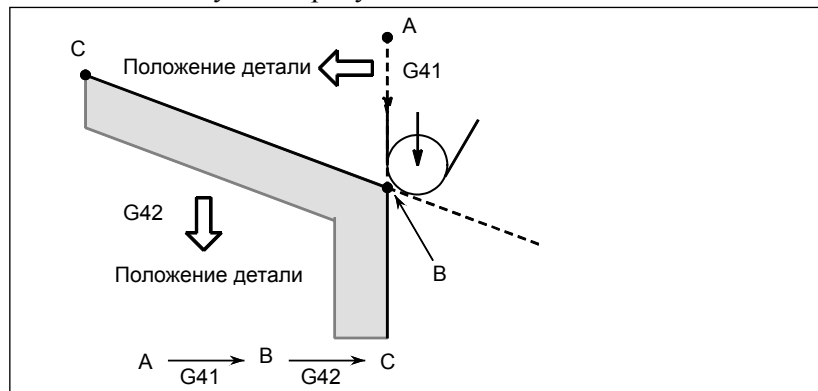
(d) Перемещение инструмента, если положение заготовки меняется
